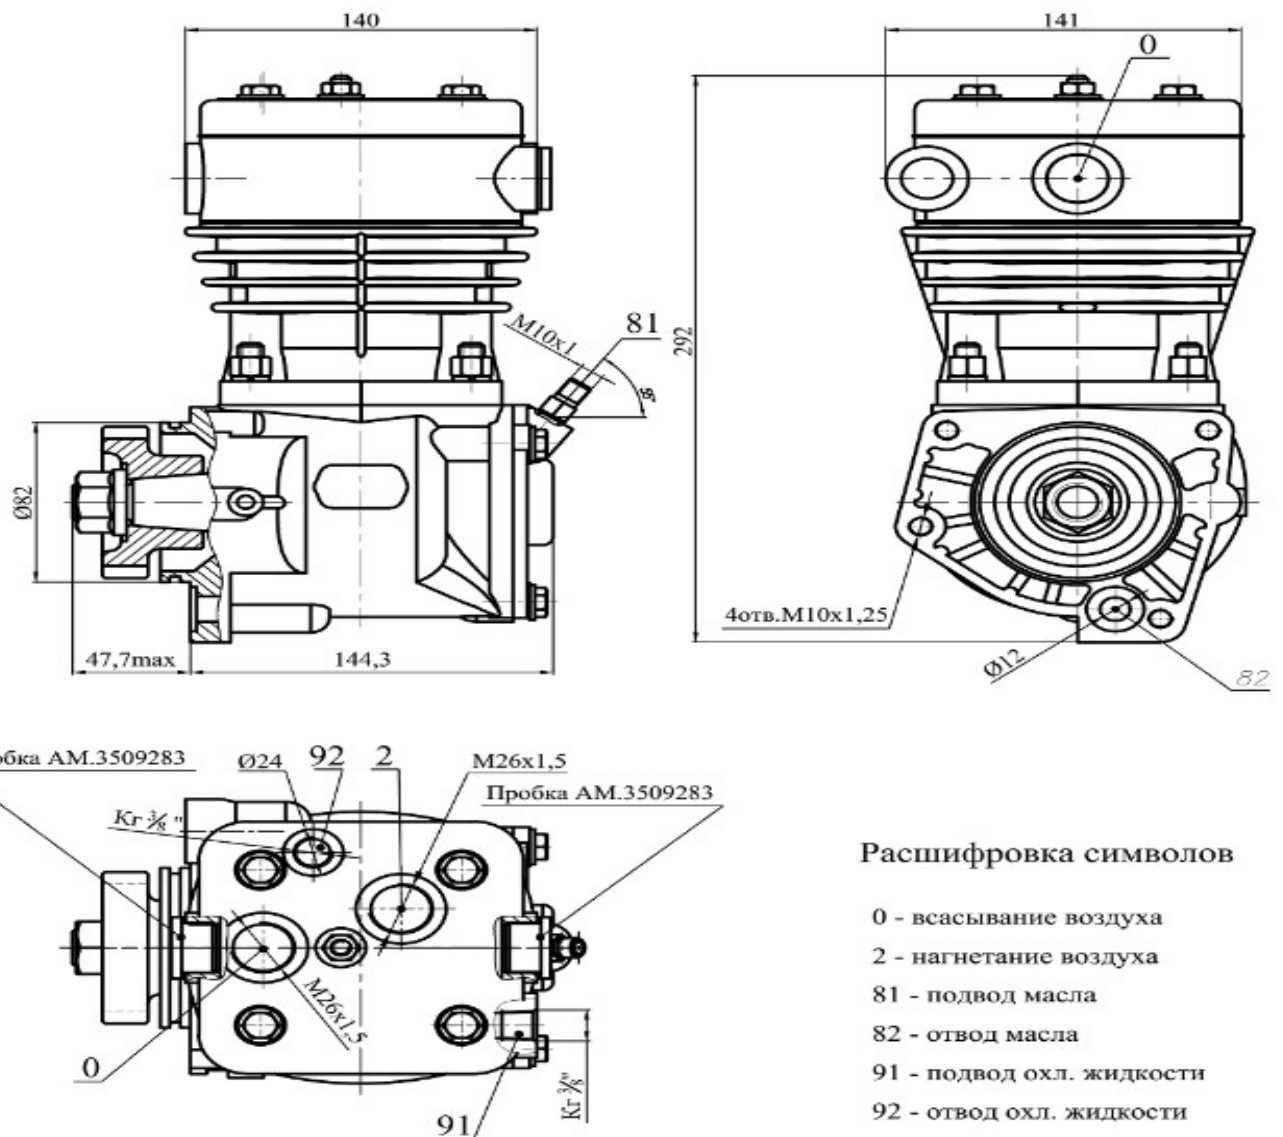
Габаритные и присоединительные размеры компрессора AM.3509015-05.
